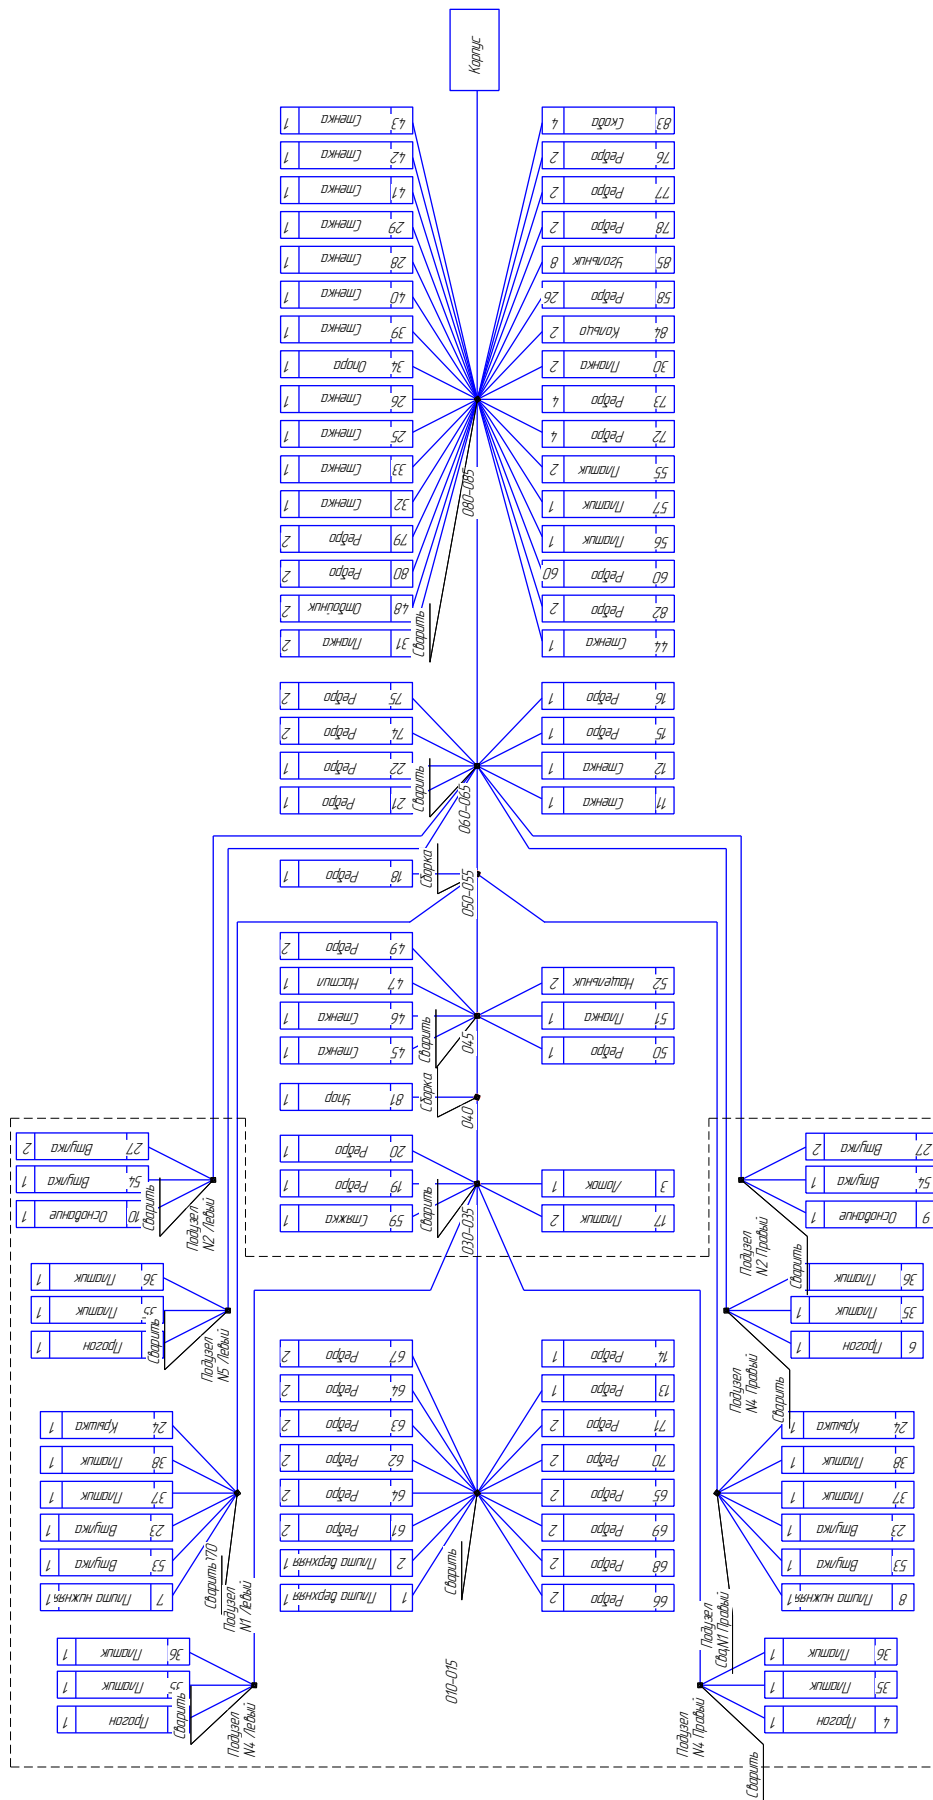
Технологическая схема изготовления корпуса питателя
